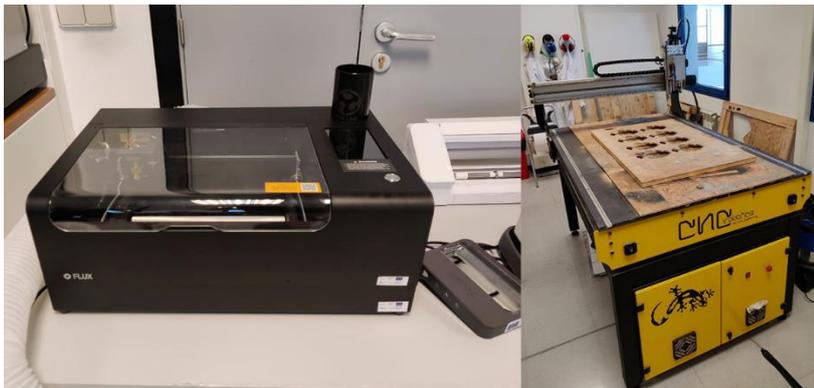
MÁQUINAS DE MECANIZADO CNC FABLAB UVa.
